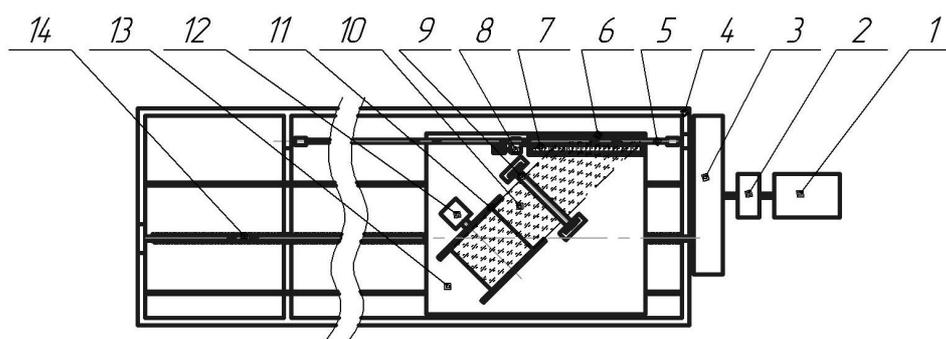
Схема установки для зміцнення насосних штанг склотканинною стрічкою
